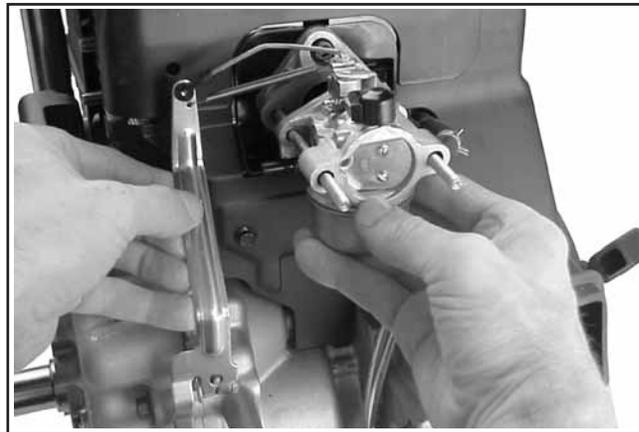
Instalar o Carburador e os Componentes do Regulador Externos.
